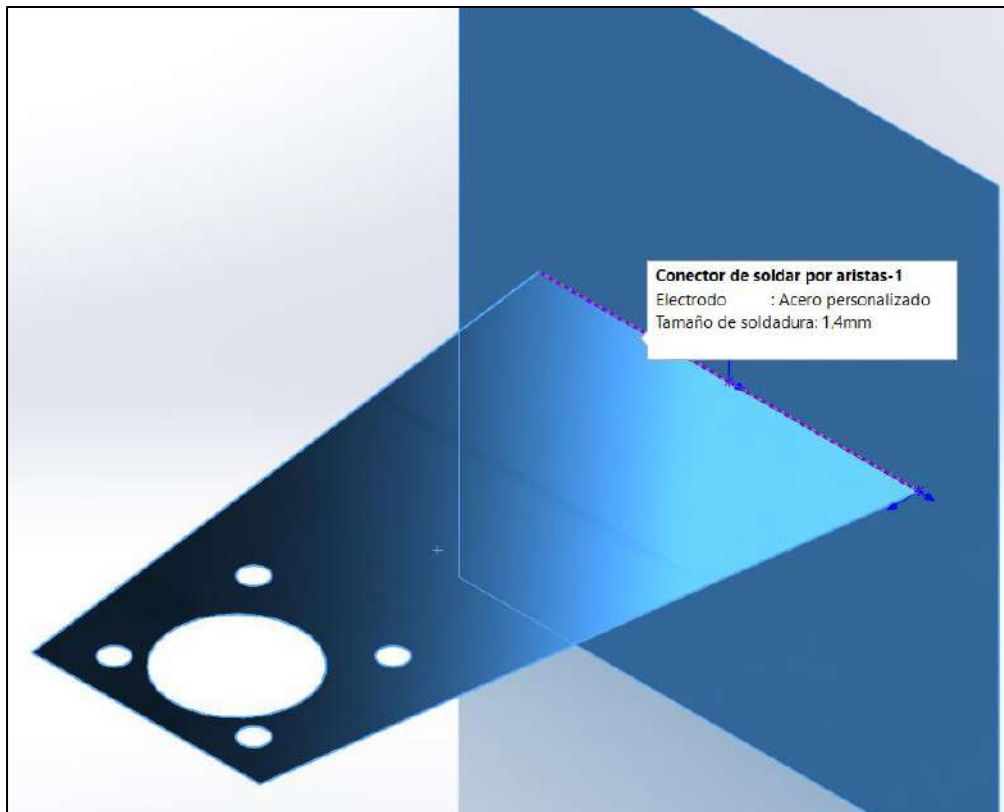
Conexión por soldadura con un tamaño de 1,4 mm.
